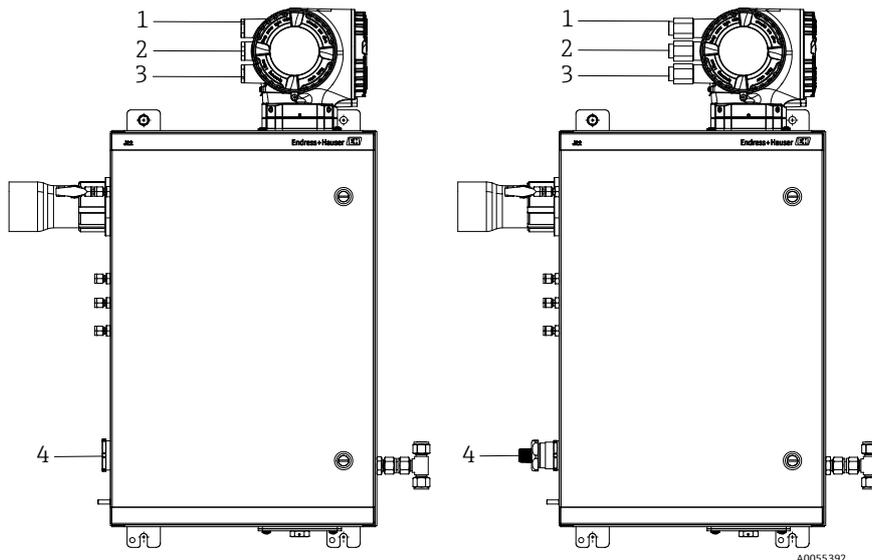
Резьбовые вводы анализатора J22 для корпуса с соединениями ATEX (слева) и дюймовыми (справа) соединениями
